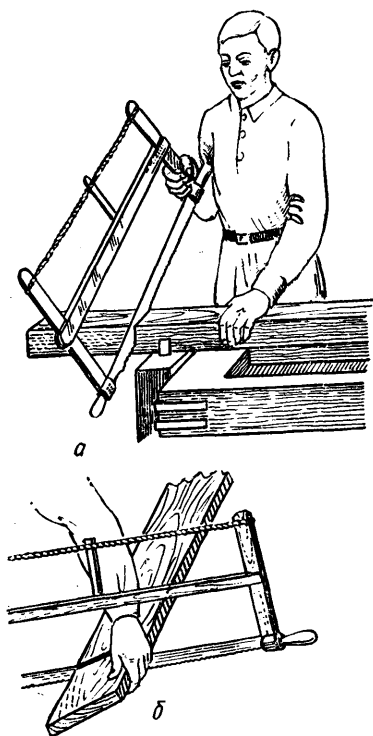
Поперечное пиление: а — прием пиления; б — отвал.
